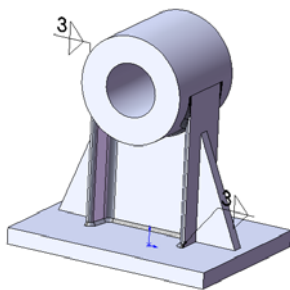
添加结构构件与基座的圆角焊缝
